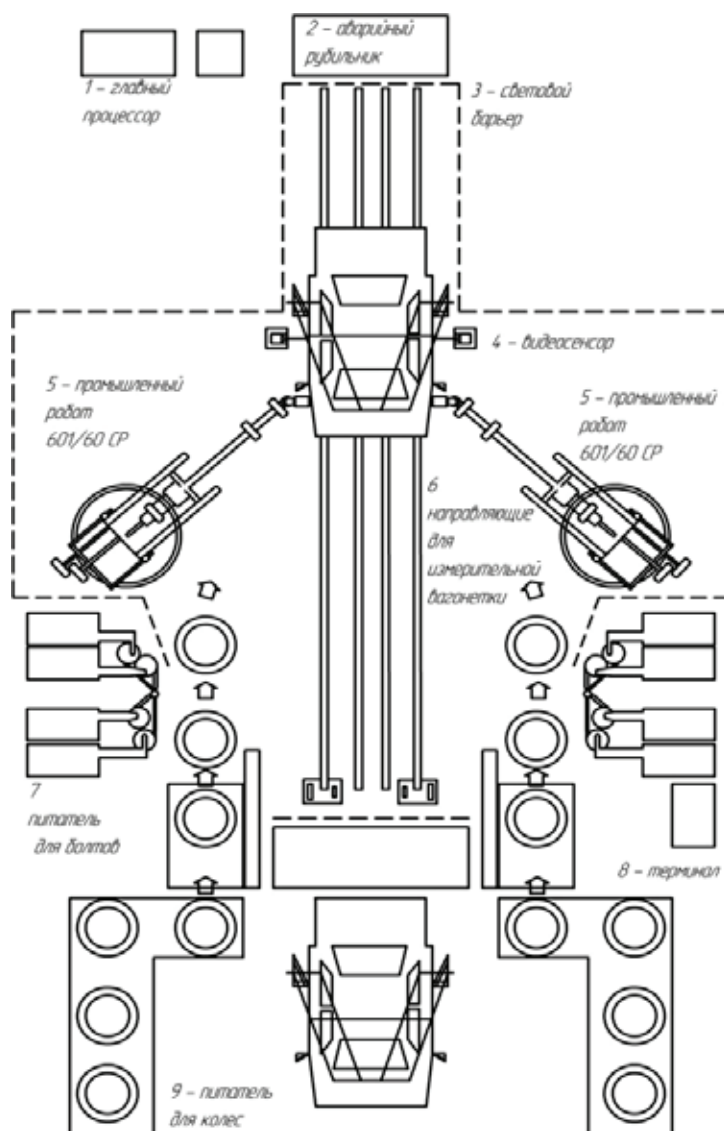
Схема комплекса: 1 — главный процессор; 2 — аварийный рубильник; 3 — световой барьер; 4 — видеосенсор; 5 — промышленный робот 601/60 CP; 6 — направляющие для измерительной вагонетки; 7 — питатель для болтов; 8 — терминал; 9 — питатель для колес
